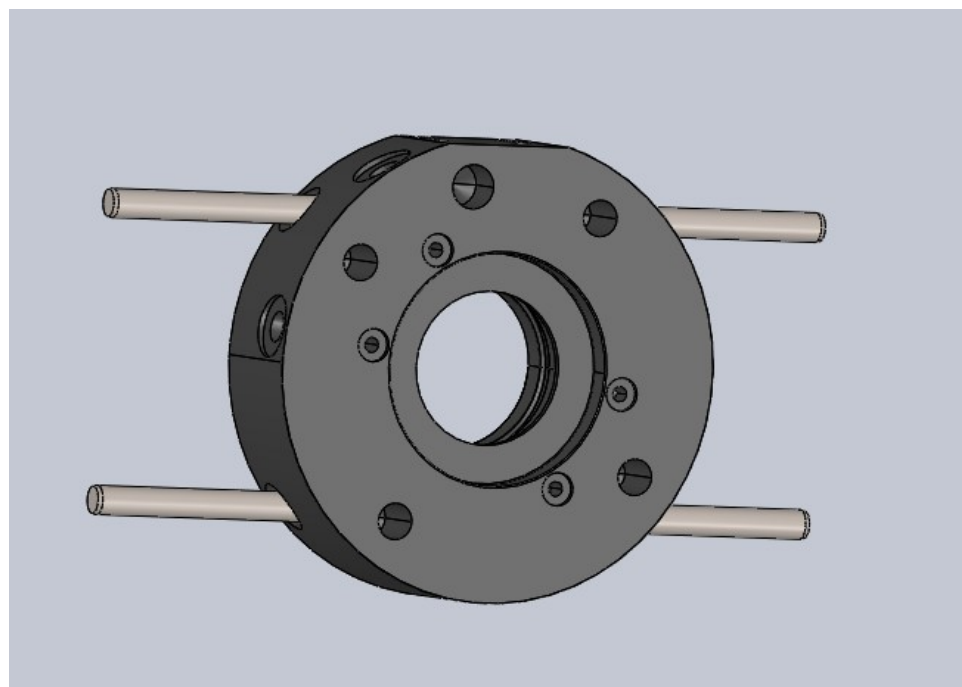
Вид пристрою для зміни інструменту з прикріпленими шпильками в
